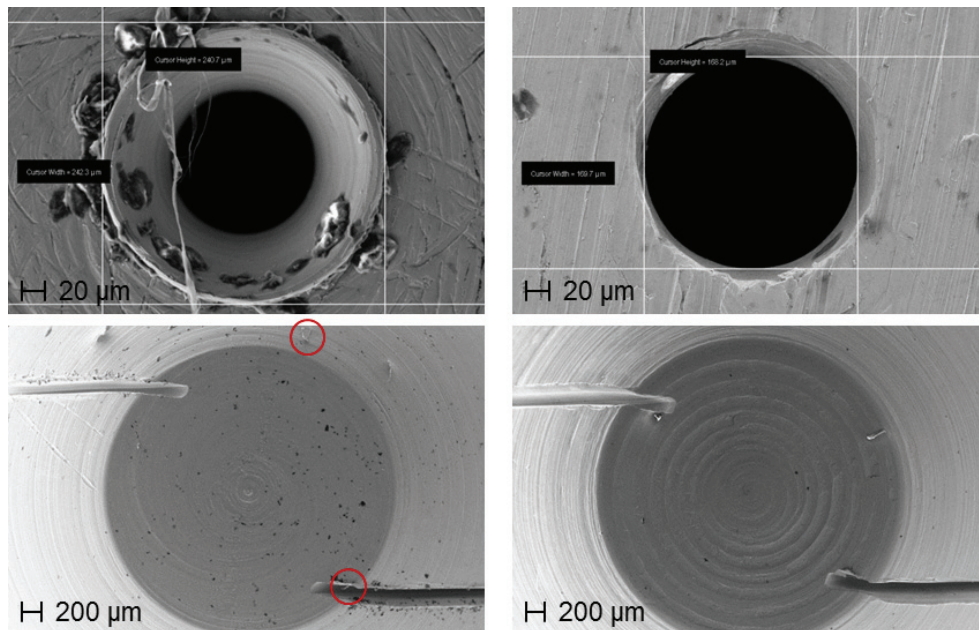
REM-Aufnahmen zur Fehleranalyse in Dralldruckdüsen, Aufsicht der Düsenöffnung und des Düsenstocks bei Dralldruckdüsen mit einem Öffnungsdurchmesser von 0,1 mm (links) und 0,15 mm (rechts)
